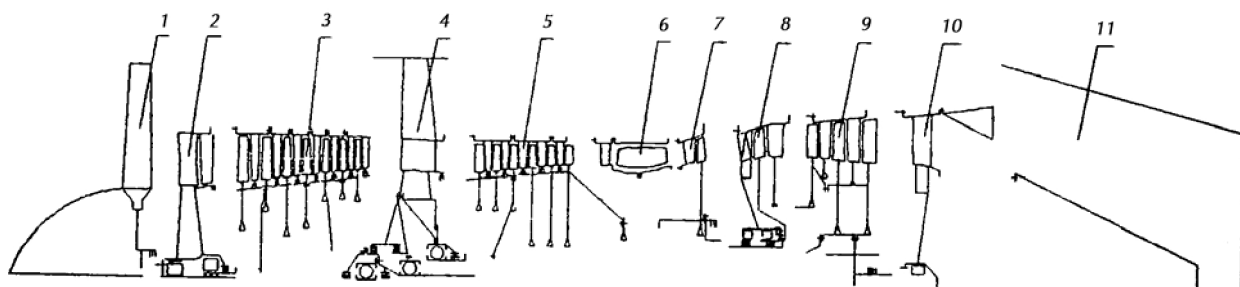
Разделение на модули; 1-вентилятор; 2-опора вентилятора; 3-компрессор СД; 4-опора компрессоров СД и БД; 5-компрессор БД; 6-камера сгорания; 7-турбина БД; 8-опора турбин БД и СД; 9-турбина НД; 10-опора турбины НД; 11-сопло.
